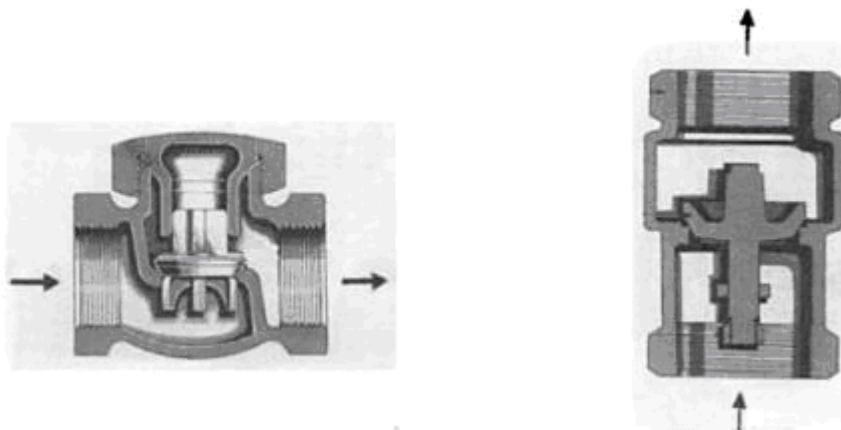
Válvula de retenção de pistão ou de levantamento (horizontal e vertical)
